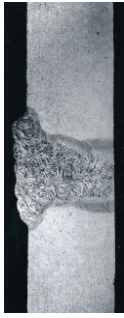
Макрошлиф сварного соединения трубы, выполненного автоматической сваркой в среде углекислого газа
